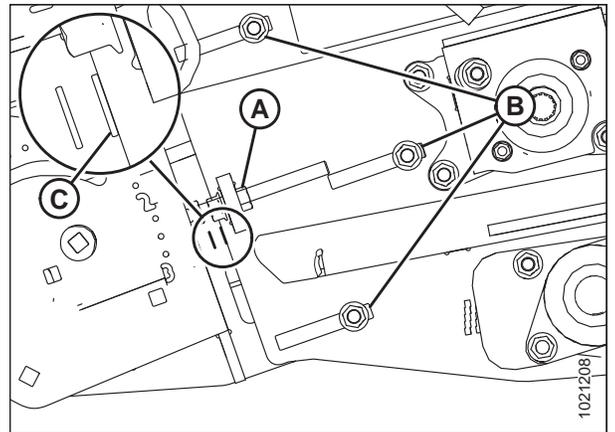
Cama delantera de lado izquierdo; lado derecho opuesto
